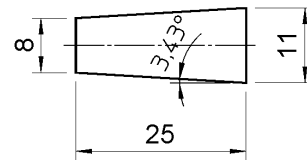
Dimensões dos bujões de tubo para tubos de CuZn20Al2 com $\varnothing 11 \times 0,8$ mm.
